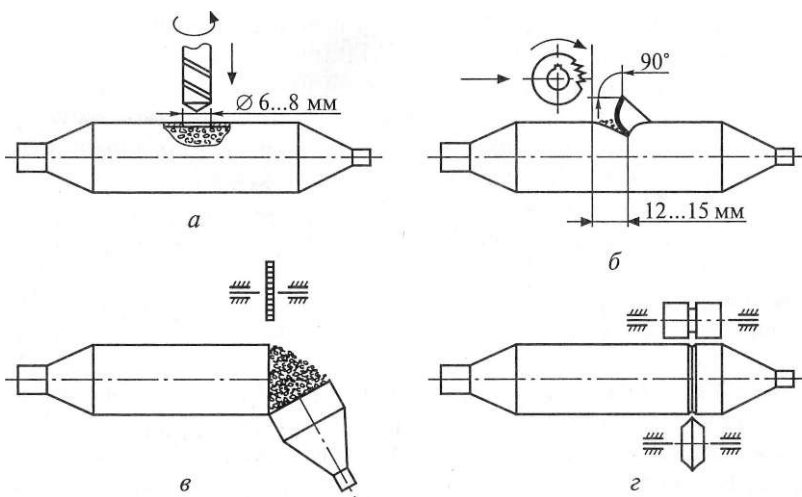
Способы извлечения адсорбента из фильтров-осушителей: а — сверление отверстия в корпусе; б — фрезерование отверстия под «лепесток»; в — фрезерование конусной образующей корпуса; г — отрезка конусной образующей корпуса
